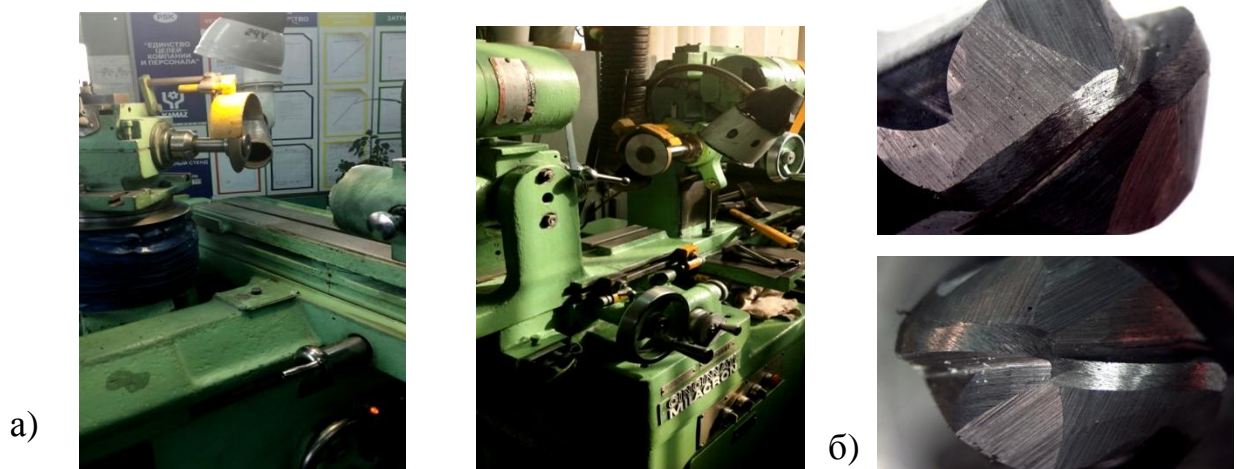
а) Универсально-заточные станки переточки концевых сферических фрез, б) рабочая часть заточенной фрезы
